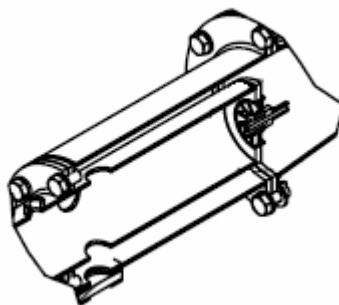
Detalhe do desenho de fabricação (Casing e Liner em corte)
